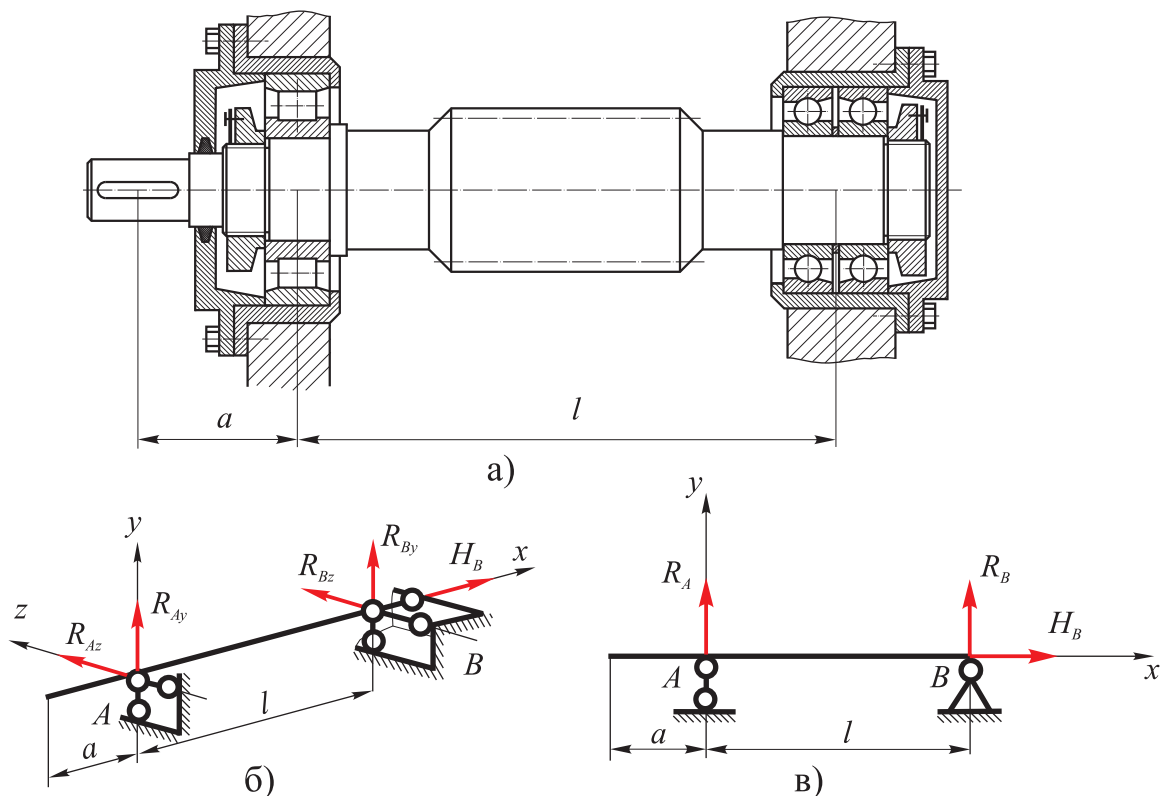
Схематизація опор вала редуктора: а – вал з опорами; б – схема опор вала для просторової системи; в – схема опор вала для плоскої системи
